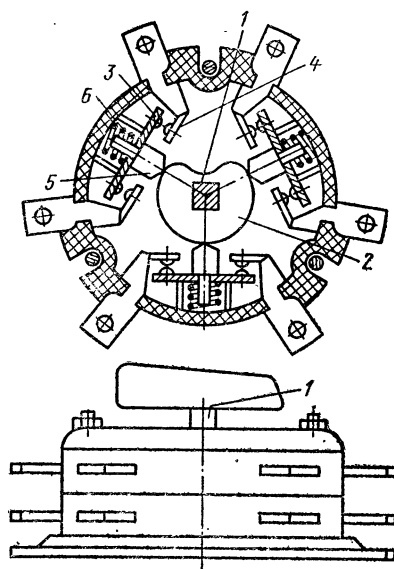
Пакетный кулачковый выключатель серии ПКВ.
